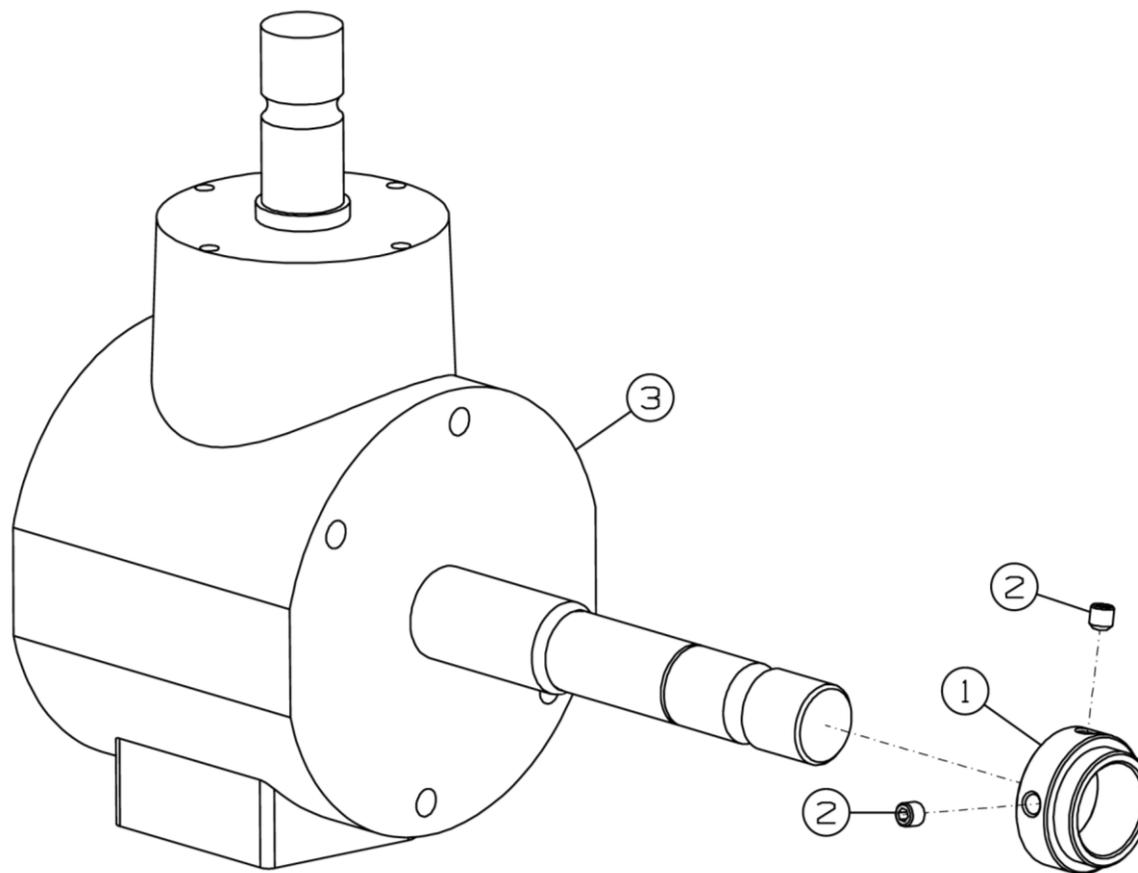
Редуктор в сборе ПКП-870.01.00.260
